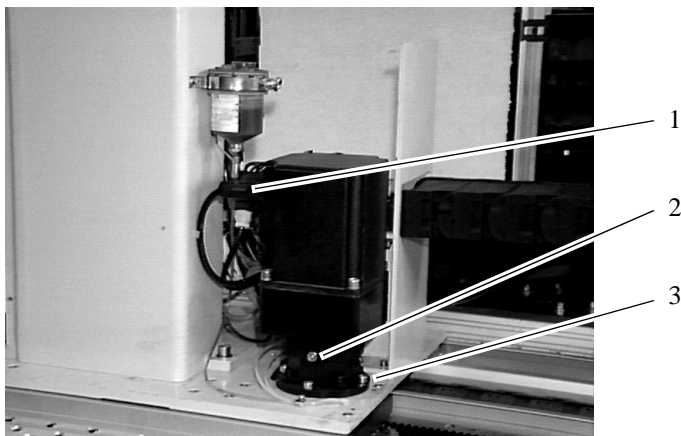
Getriebe mit Motor 5 (H-Achse)
